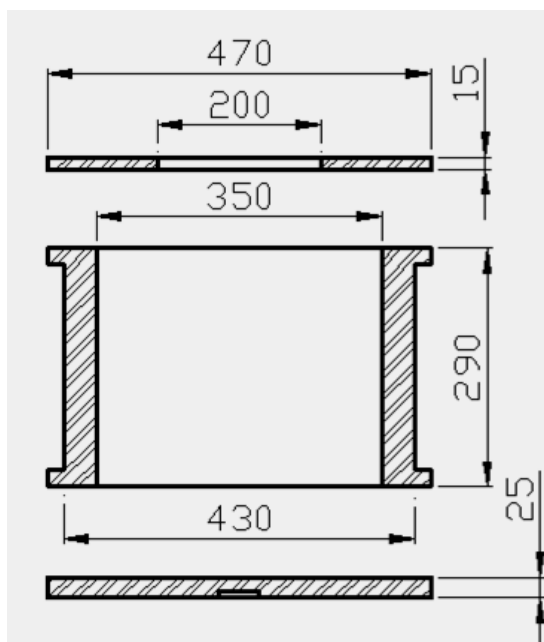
ESQUEMA DE LAS DIMENSIONES DEL MOLDE.
